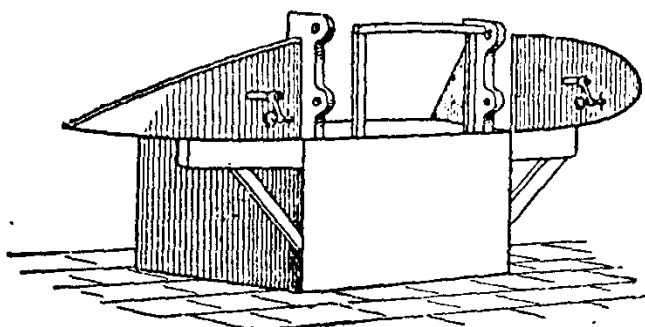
Стапель общей сборки каркаса консоли крыла.
